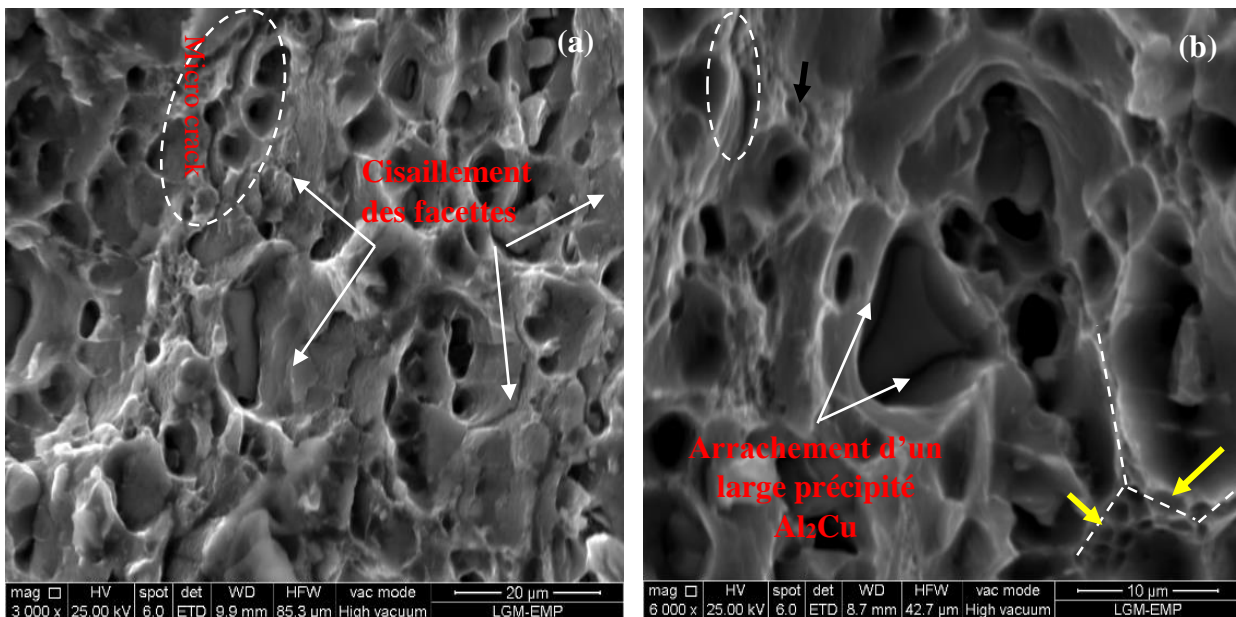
Fractographie à un grossissement supérieur indiquant le mécanisme de fracture.
